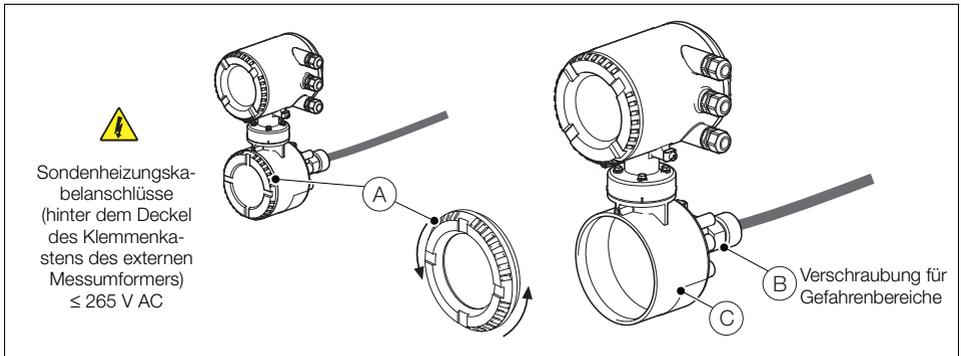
Zugang zu den Anschlussklemmen – Klemmenkasten des externen Messumformers
